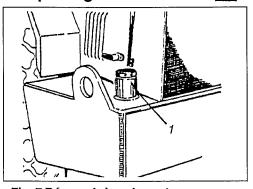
Réservoir à carburant 1 Tuyau de remplissage
